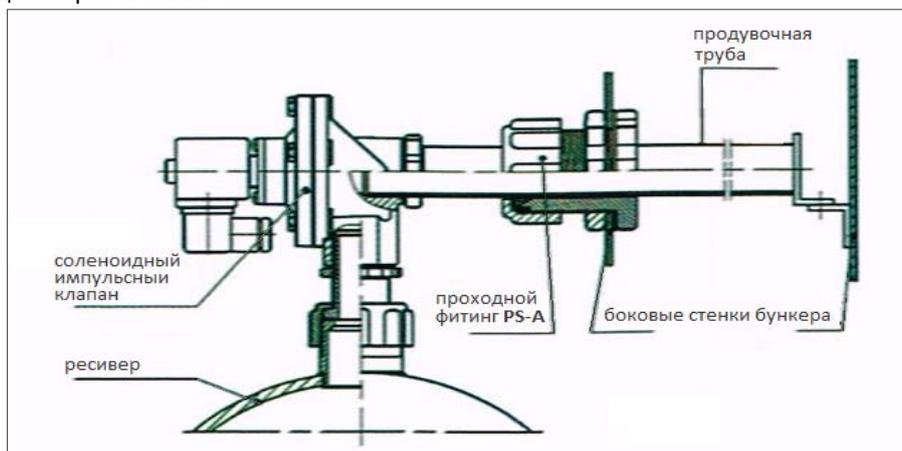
Монтажный чертёж установки проходного одностороннего фитинга PS-A
